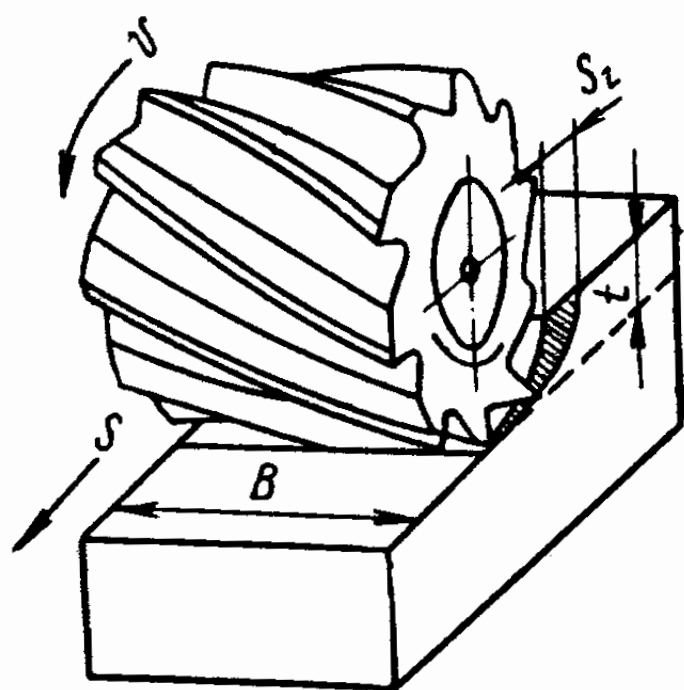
Элементы режима резания при фрезеровании цилиндрической фрезой.
